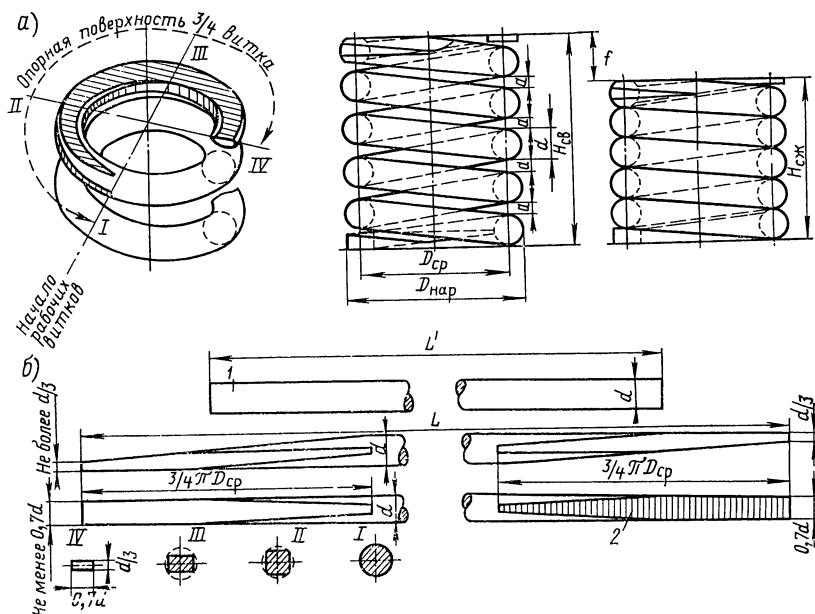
Цилиндрическая пружина (а) и заготовка (б):
